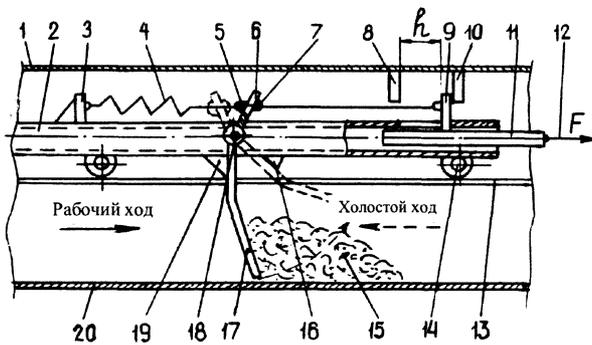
Фрагмент скребкового конвейера с механизмом принудительного подъема и опускания рабочих органов:
